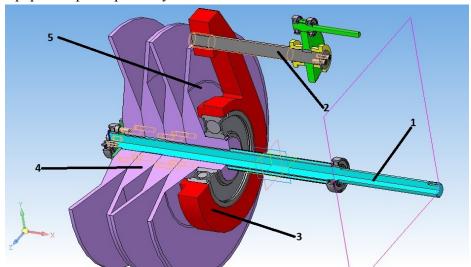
Предлагаемая конструкция клиноременного вариатора
